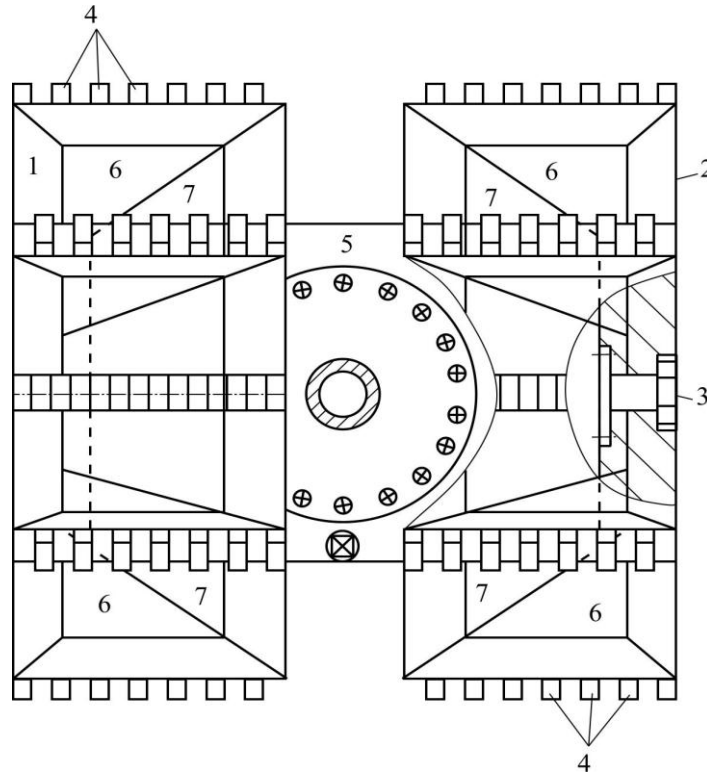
Загальний вигляд породоруйнюючого агрегату з роторними колесами: 1, 2 – роторні колеса; 3 – кріплення; 4 – ріжучі елементи; 5 – несучий став; 6 – косинки; 7 – піддони.
